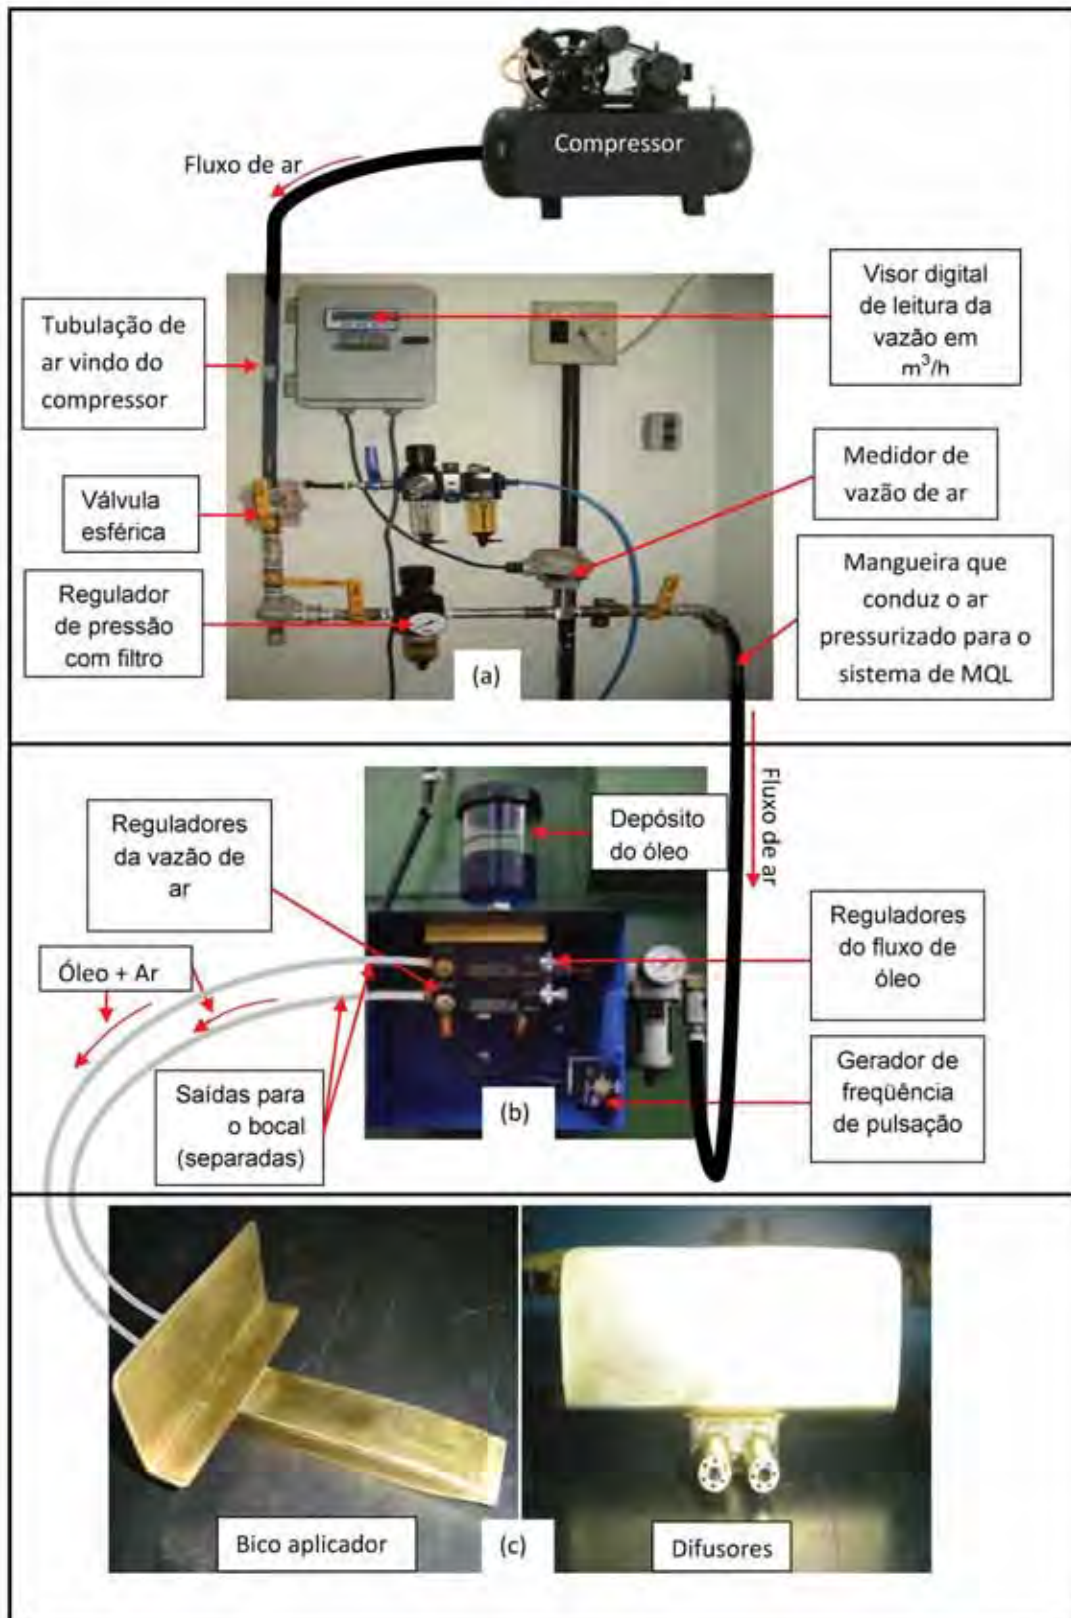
Bocal fabricado para a técnica de lubri-refrigeração otimizada
